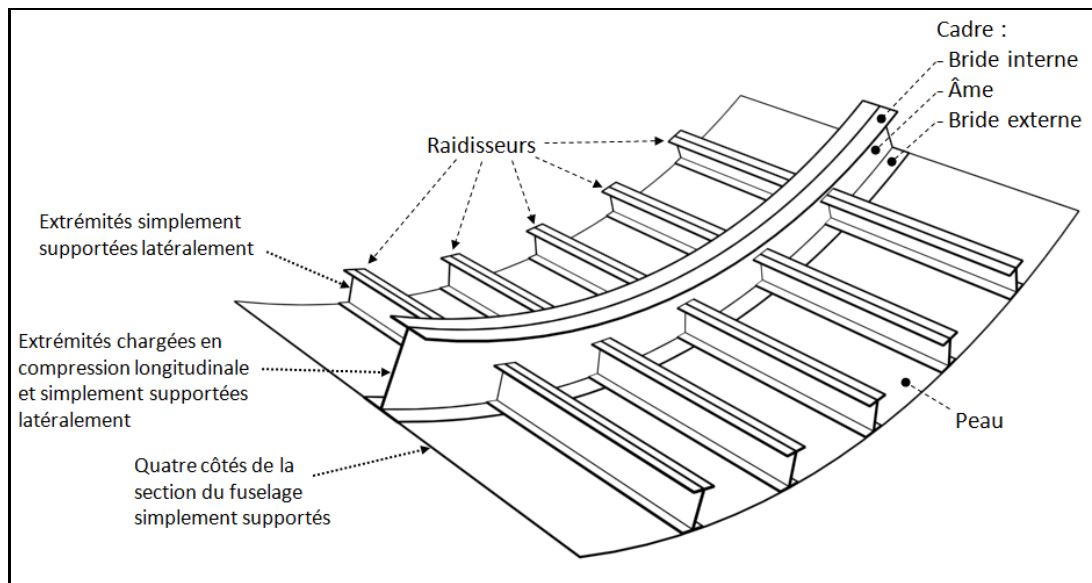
Section de fuselage incluant un cadre à dimensionner
